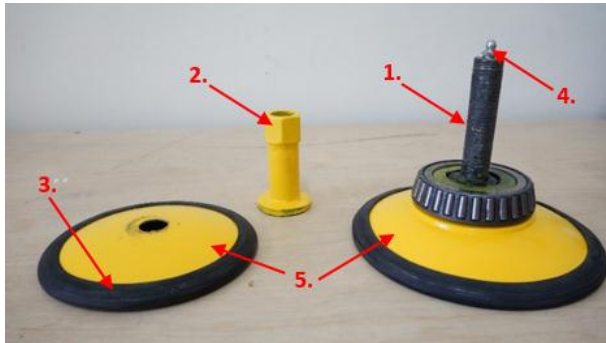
Pressure Bearing Lubrication Special Tool
